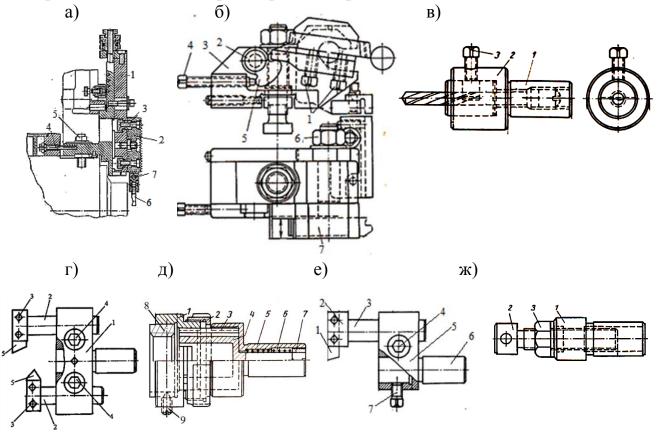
Схемы наладки режущего и вспомогательного инструментов:
